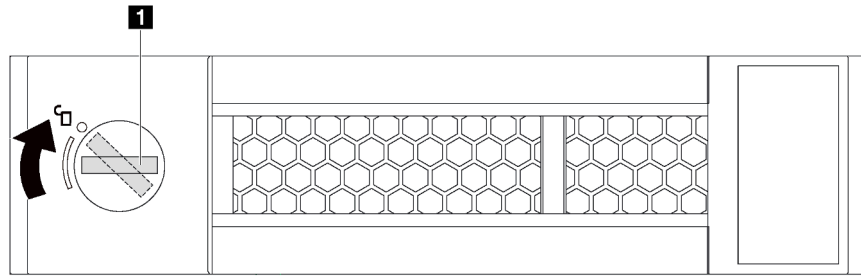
Ouverture de la poignée du tiroir d'une unité 3,5 pouces à remplacement standard
